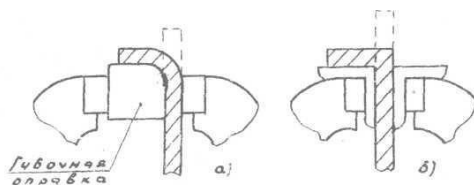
Приемы закрепления заготовки в тисках при гибке.
